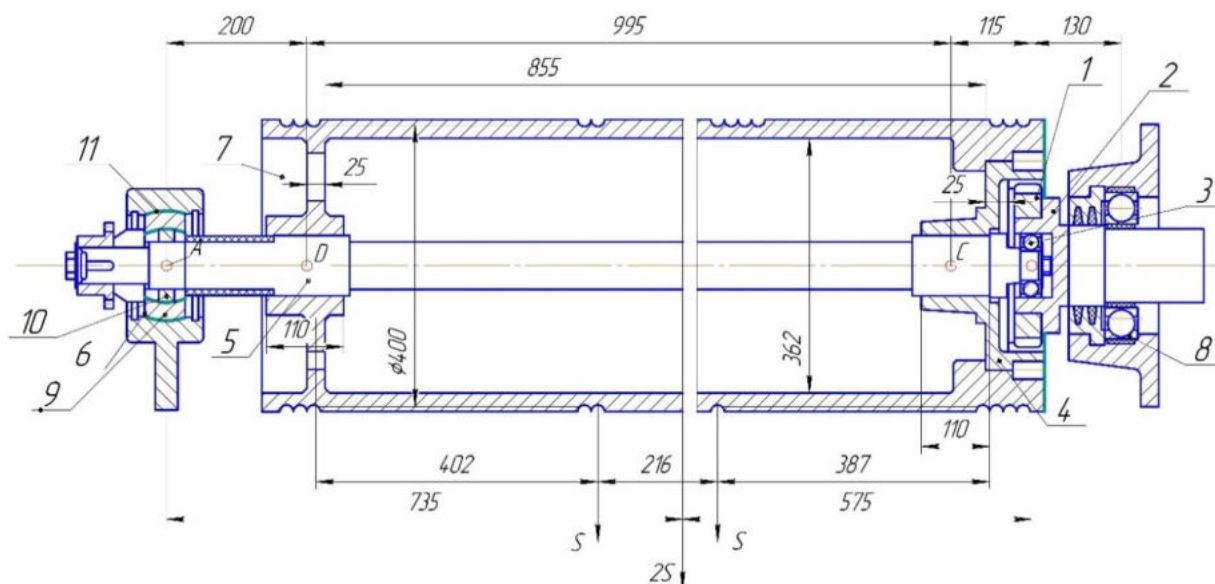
Узел барабана: 1 – зубчатый диск; 2 – вал редуктора; 3 – опорное кольцо; 4 – венец; 5 – ось; 6 – опорный подшипник; 7 – барабан; 8 – правая стойка; 9 – наружная шаровая опора; 10 – внутренняя шаровая опора; 11 – тканевое покрытие
